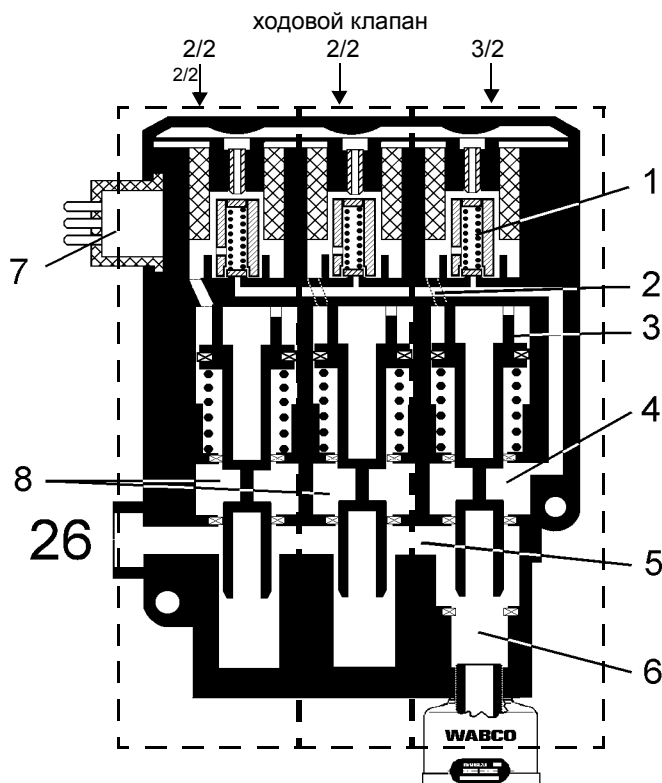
Изображение в разрезе магнитного клапана ECAS с золотниковыми клапанами пружинно-возвратного типа для задней оси или части главной оси (блок магнитов)
